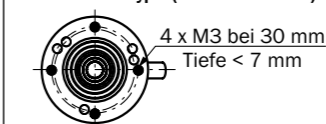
Anbau DBS36 Klemmflansch über flanschseitige Gewindebohrungen
